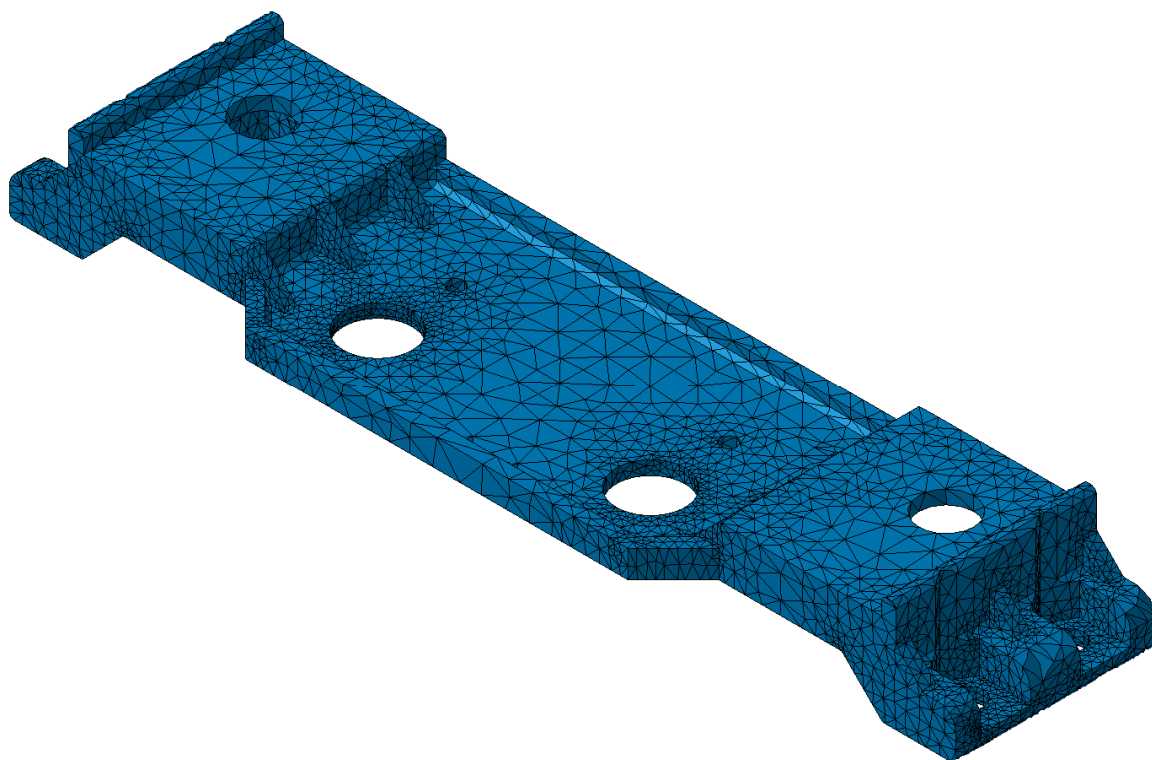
3D model – 3. varianta držáku – horní pohled
